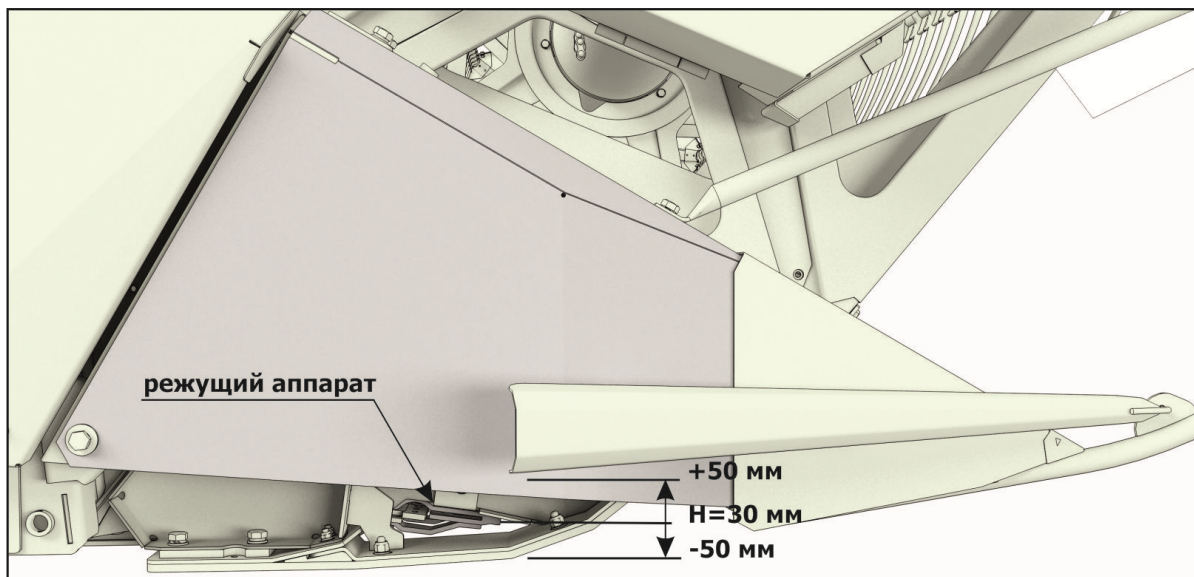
Положение режущего аппарата для уборки сои
